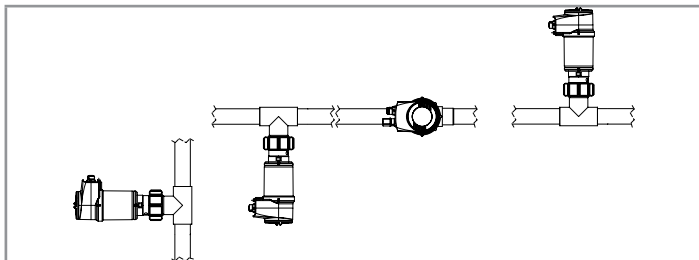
Posições de montagem da unidade de encaixe/ dispositivo no tubo
